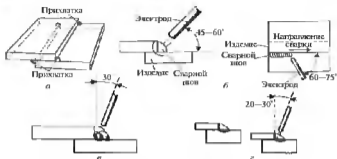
Сварка нахлесточного соединения в нижнем положении: *а* — подготовка соединения к сварке, *б* — положение электрода при сварке односторонним швом равных толщин, *в* — положение электрода при втором и третьем проходе при выполнении двустороннего шва, *г* — положение электрода при сварке разных толщин
